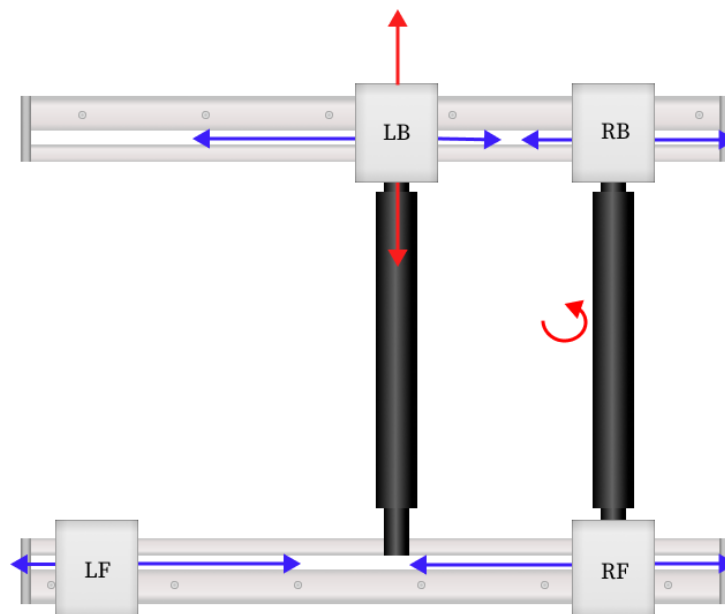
Snímek upraveného modelu v nástroji CAD Toolbox
